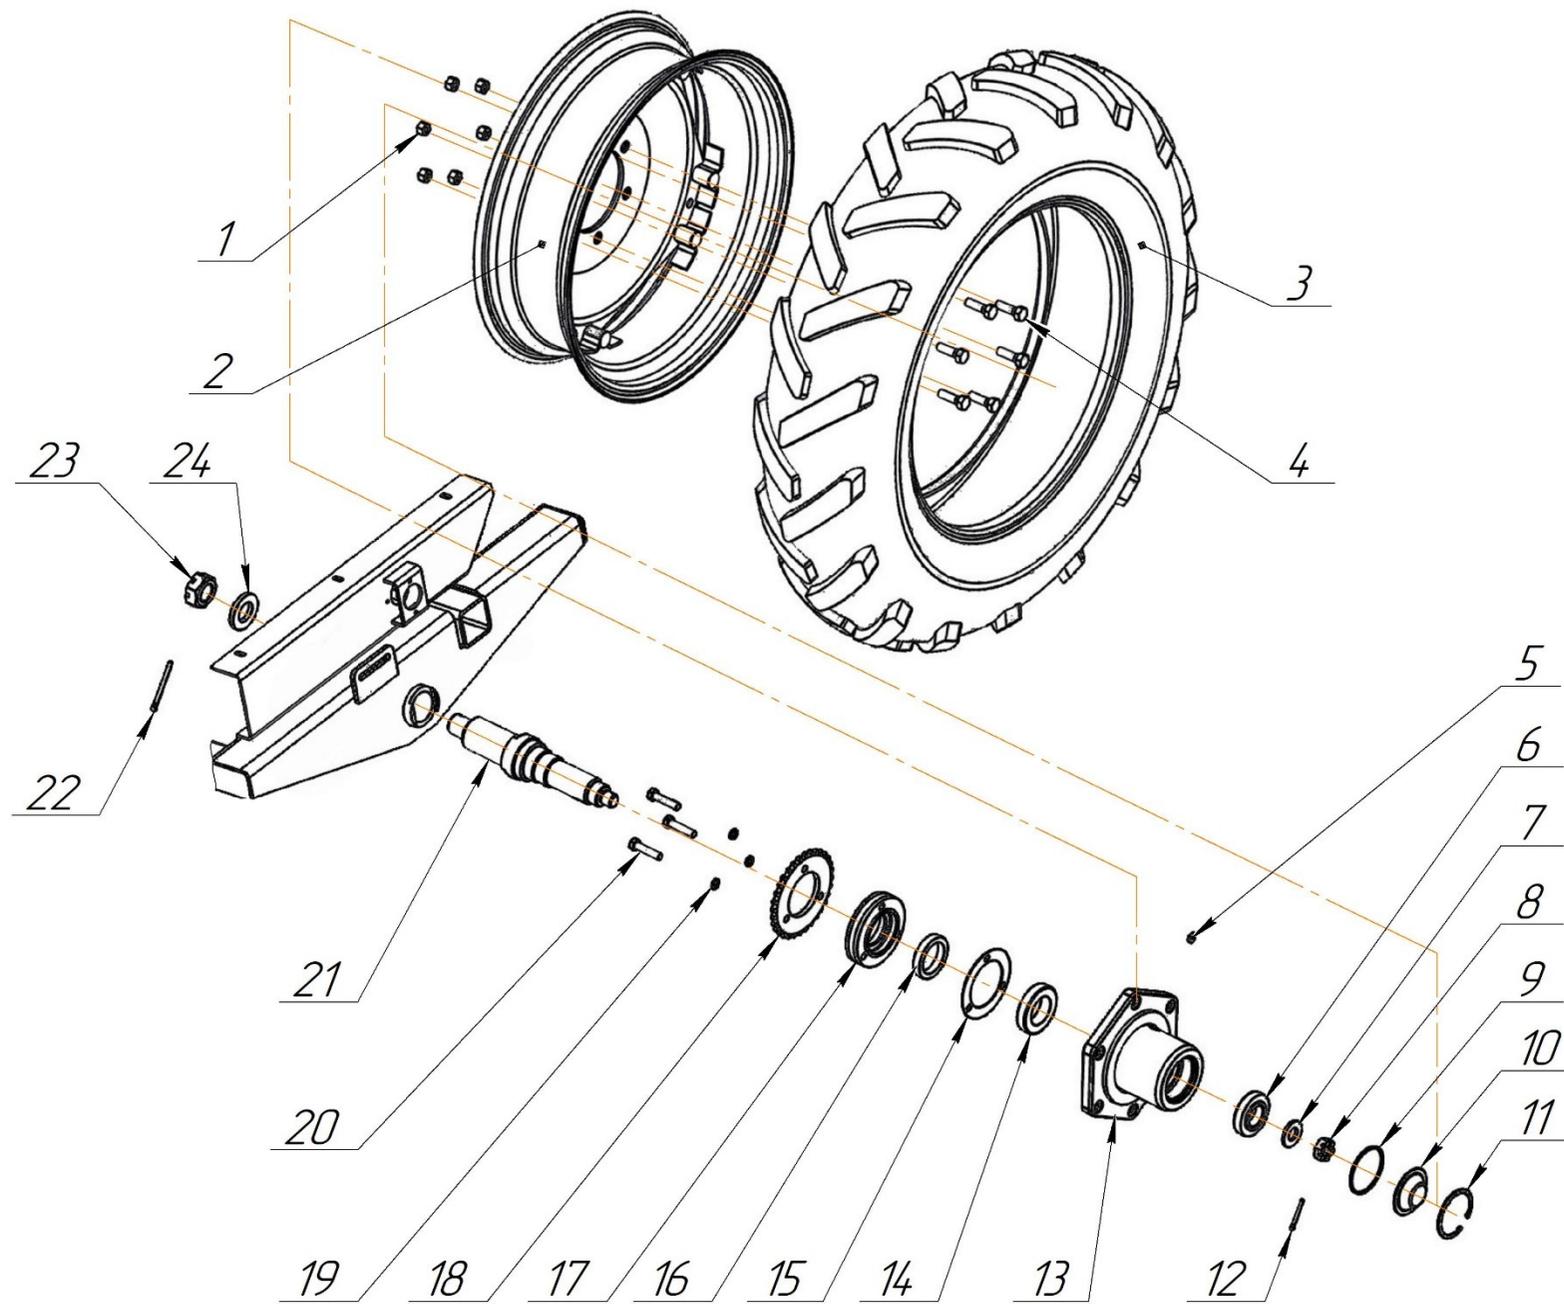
Колесо опорно-приводное и ступица СЗМ 00.2000-01 в сборе
